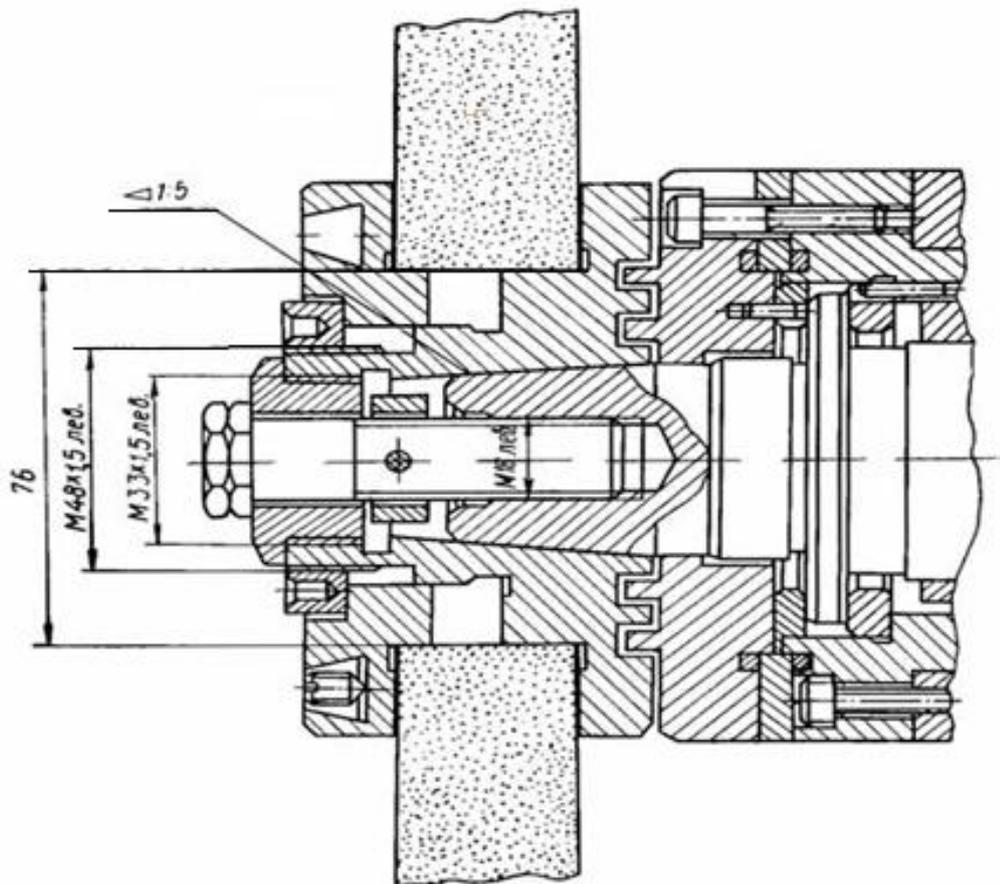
Основные размеры посадочного места шлифовального круга станка 3Г71
